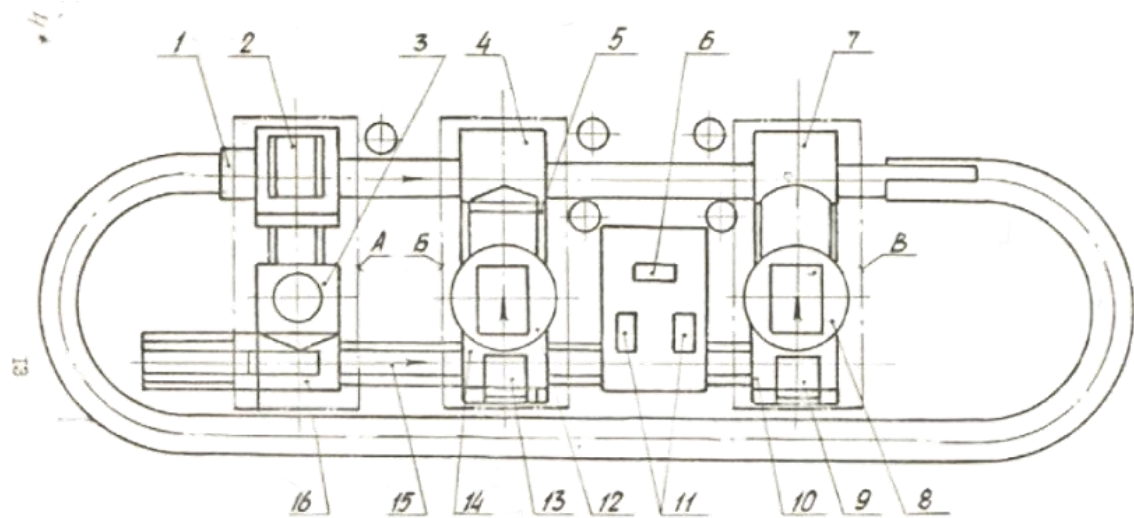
Схема автоматичної формувальної лінії моделі 696: А - позиція вибивки; Б - виготовлення напівформ низу; В - встановлення напівформ верху; 1 - конвеєр; 2 - механізм зіштовхування форм; 3 - механізм видавлювання кома; 4 - установник напівформ низу на 1; 5 - кантувач форм низу; 6 - пневмокомандоапарат управління АФЛ; 7 - збиральник форм; 8 - формувальний автомат (ФА); 10 - механізм знімання верхніх опок; 11 - пневмокомандоапарати управління ФА 8 и 12; 12 - ФА виготовлення напівформ низу ; 13 - механізм подачі нижніх опок у ФА; 14 - розпарювач опок; 15 - роликовий конвеєр; 16 - механізм підйому нерозпарованих опок;  - робочі місця.
